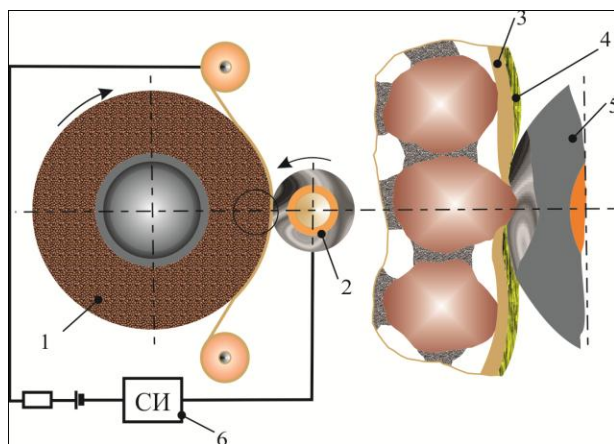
Схема экспресс-метода определения числа зерен на рабочей поверхности инструмента:
